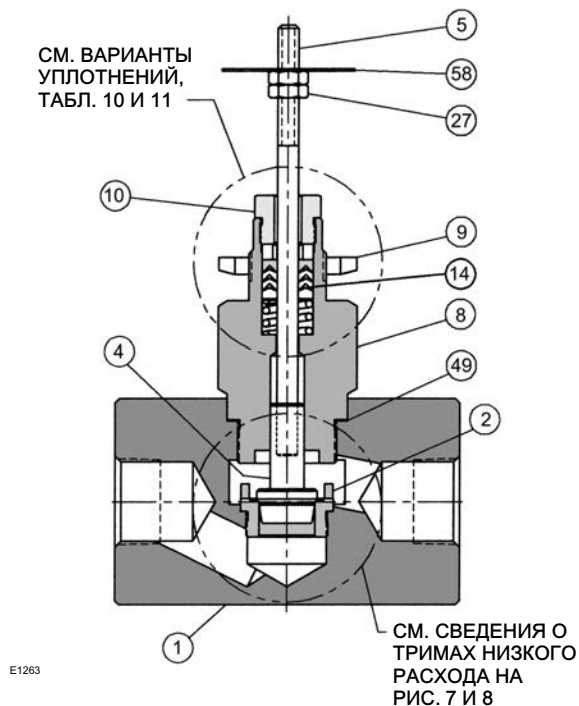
Корпус клапана Вауманн с удлиненной крышкой
